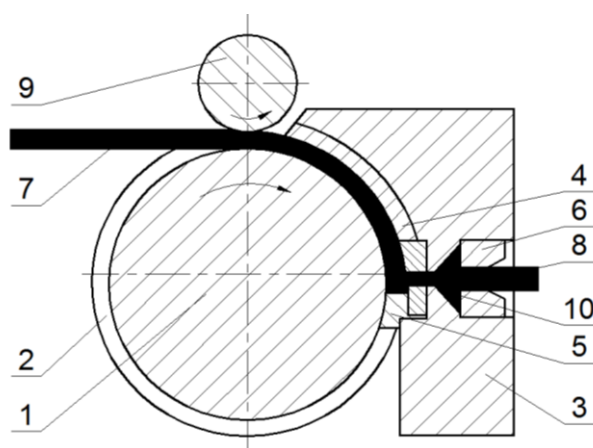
Схема Конформ с форкамерой: 1 –рабочее колесо, 2 – ручей колеса, 3 – башмак, 4 – кольцевая вставка, 5 – опорная вставка, 6 – матрица, 7 – прутковая заготовка, 8 – пресс-изделие, 9 – прижимной ролик
